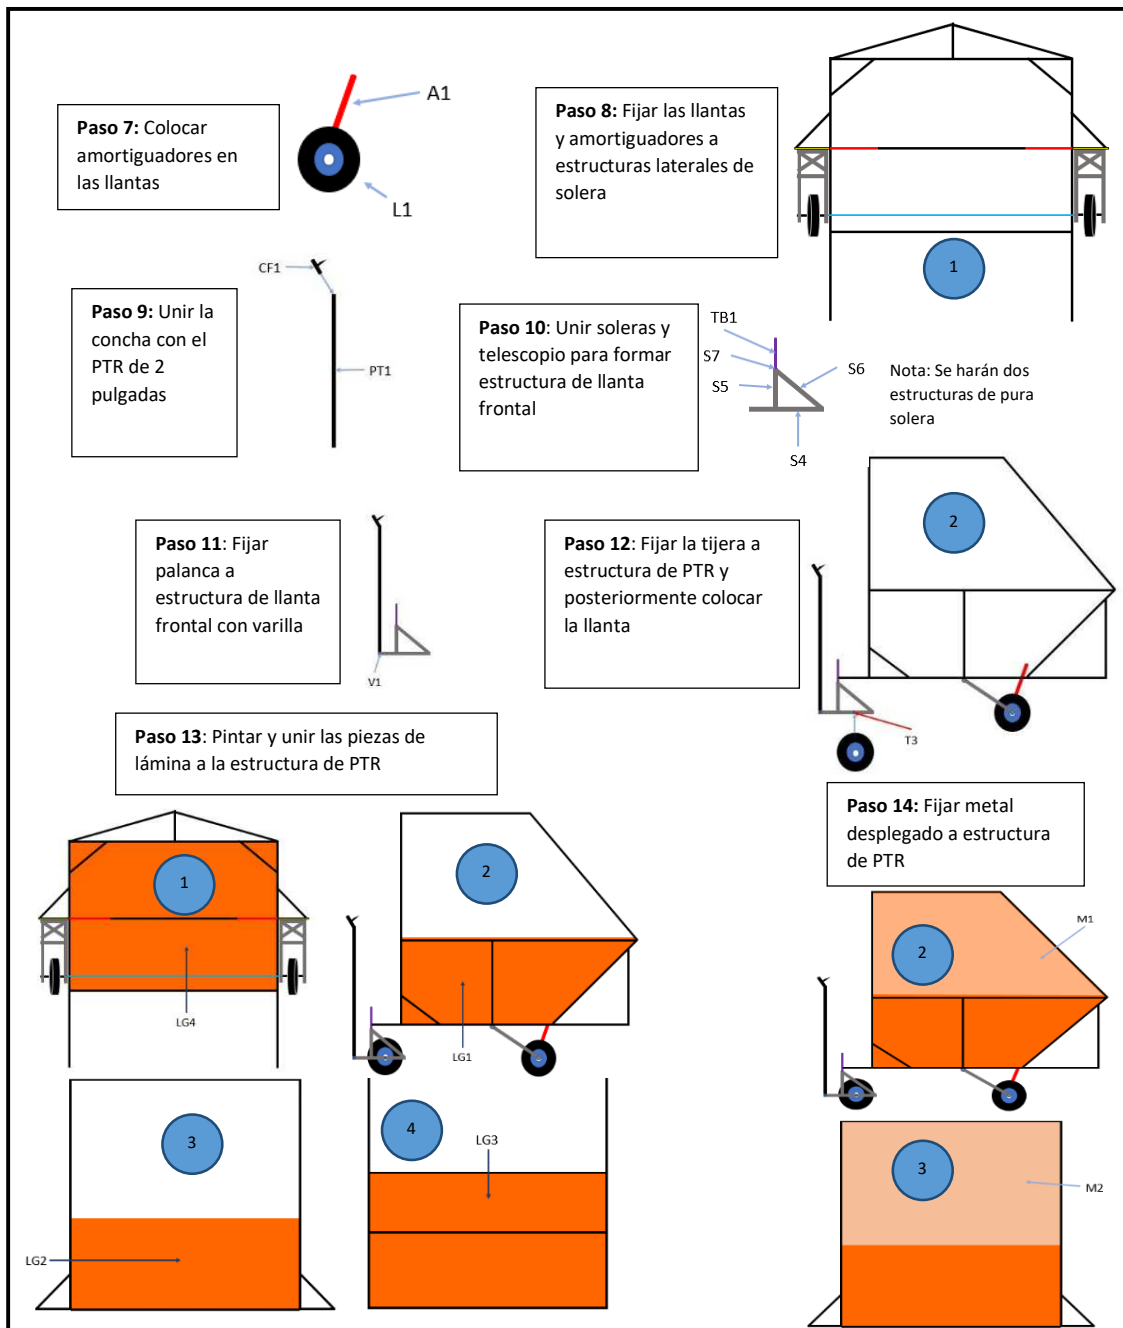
Instructivo de armado de Carreta, Parte 2. Fuente: Elaboración propia.
